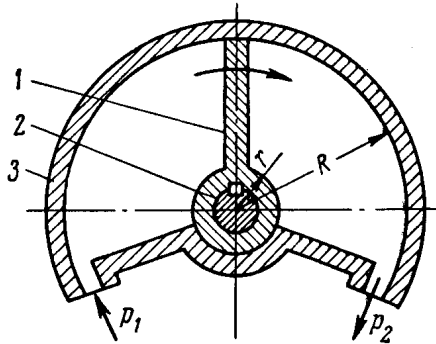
Моментний гідроциліндр: 1 – поворотна пластина; 2 – вихідний вал; 3 – циліндр; p_1 – тиск в робочому положенні; p_2 – тиск у зливній порожнині
